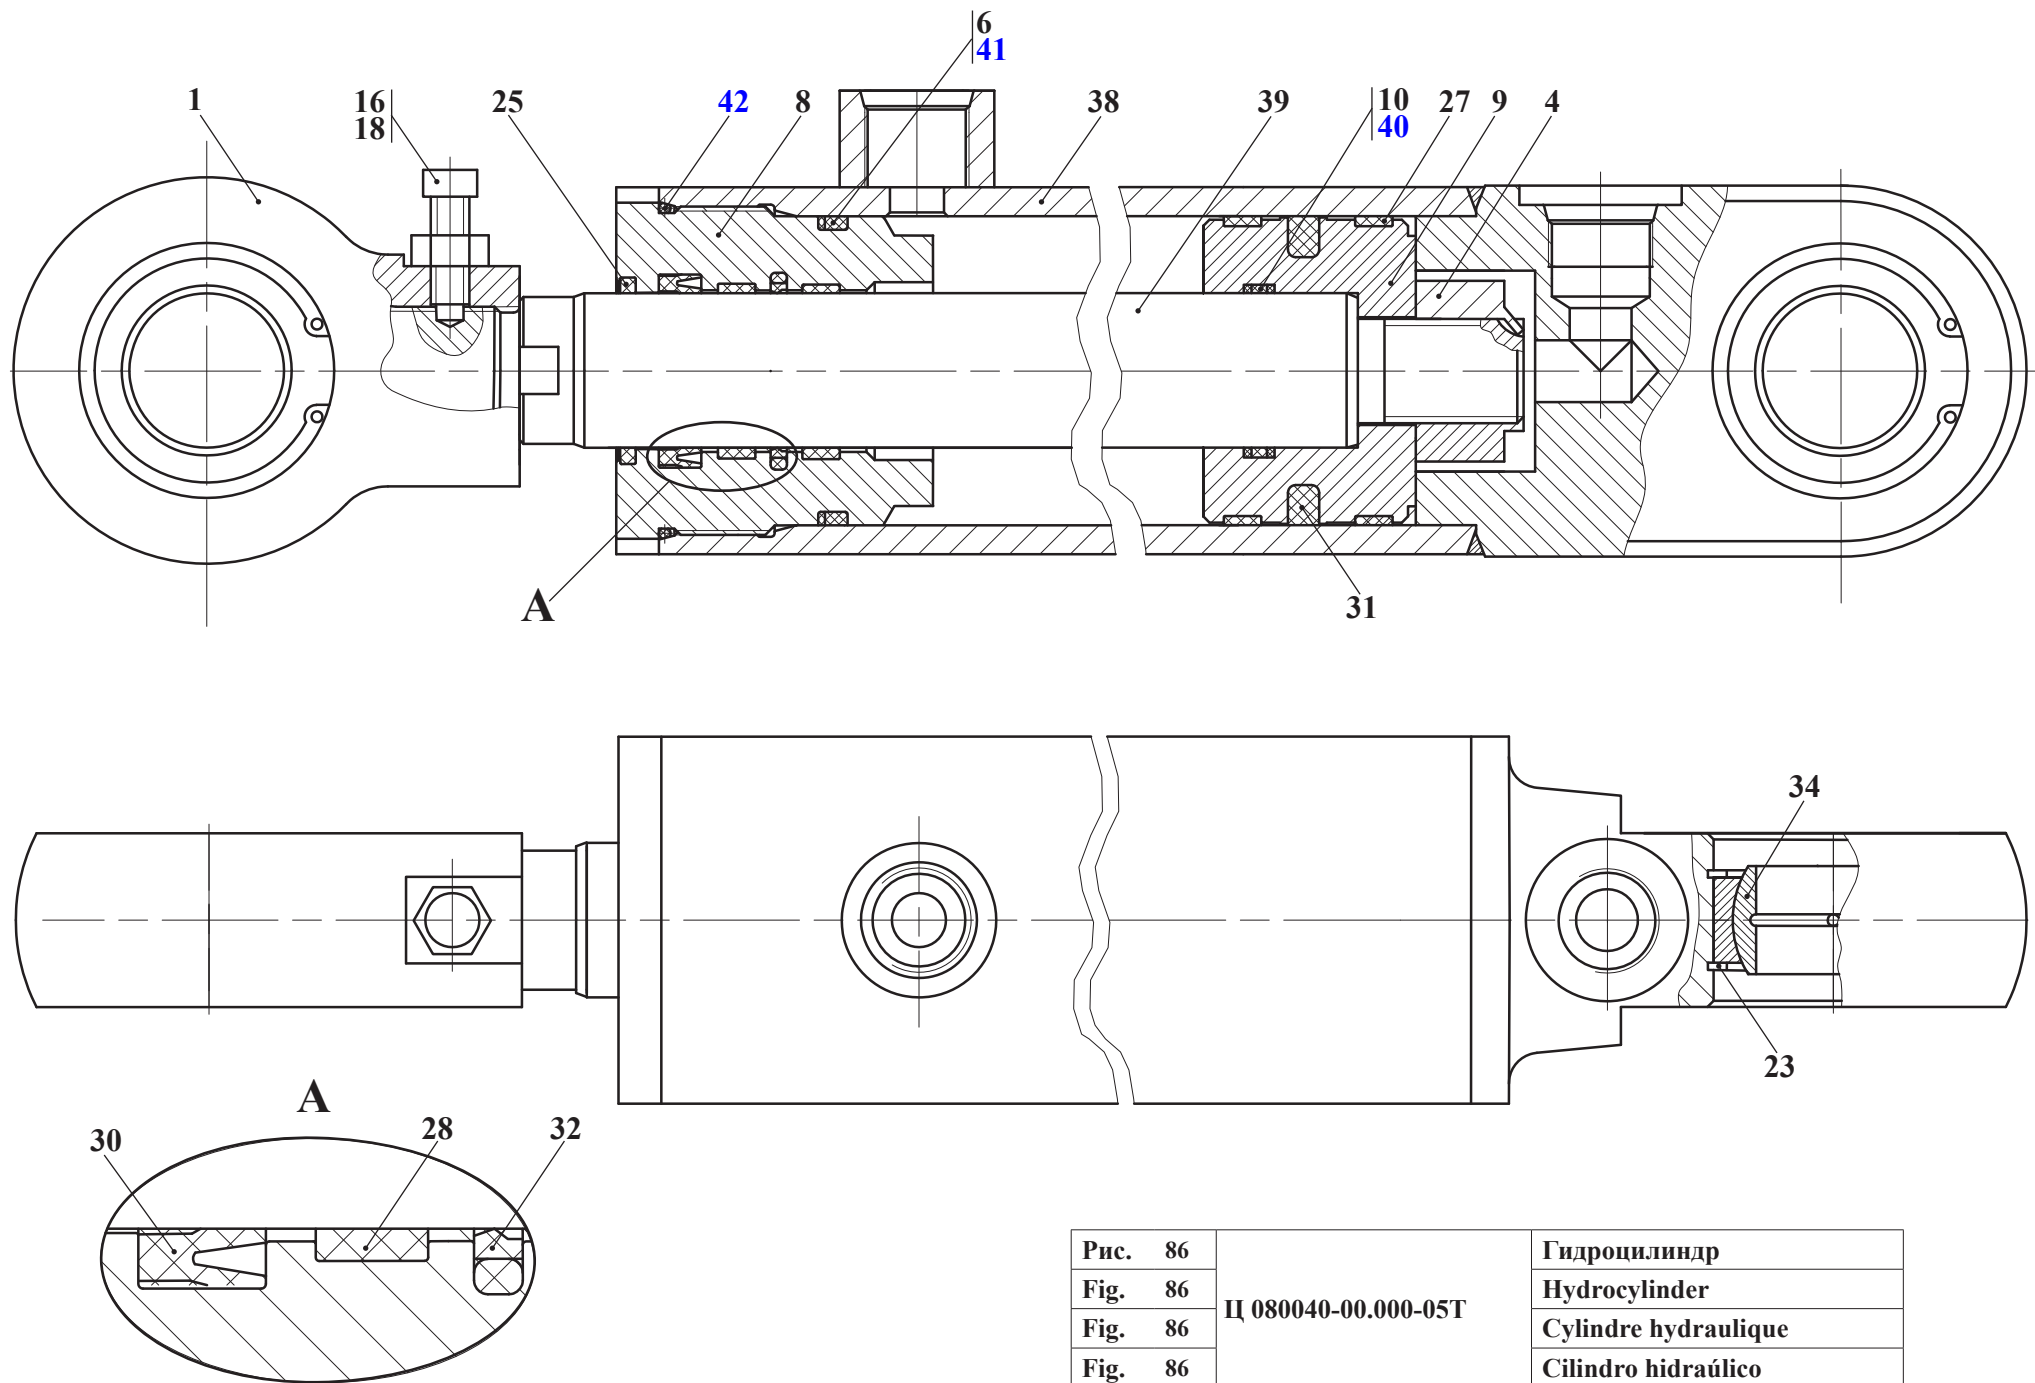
Ц 080040-00.000-05Т	Гидроцилиндр
